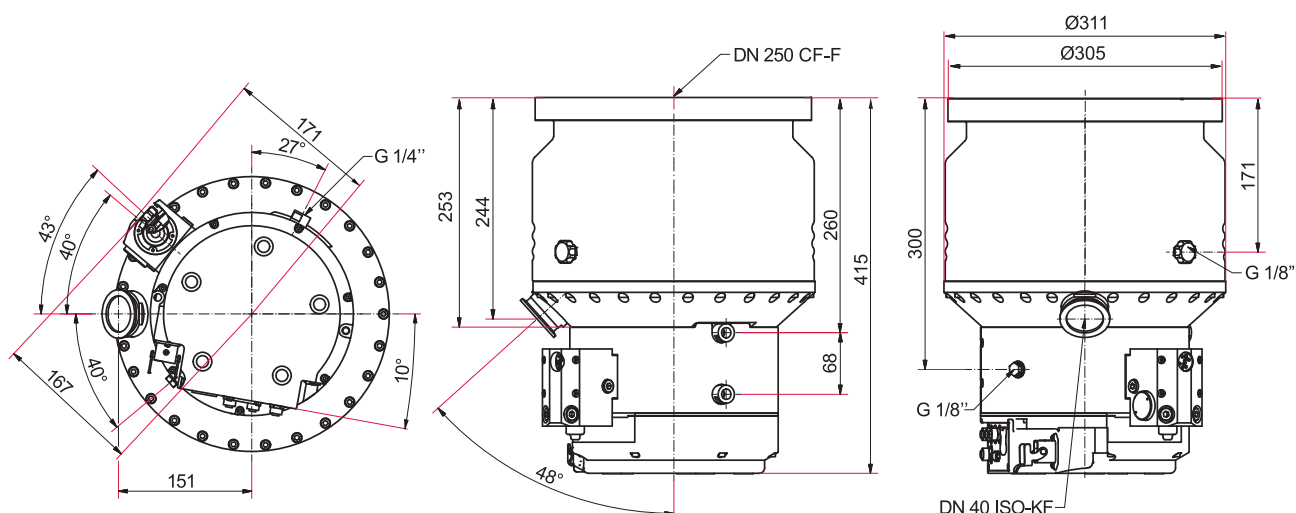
Dimensions HiPace 2300 et HiPace 2300 C | DN 250 CF-F
